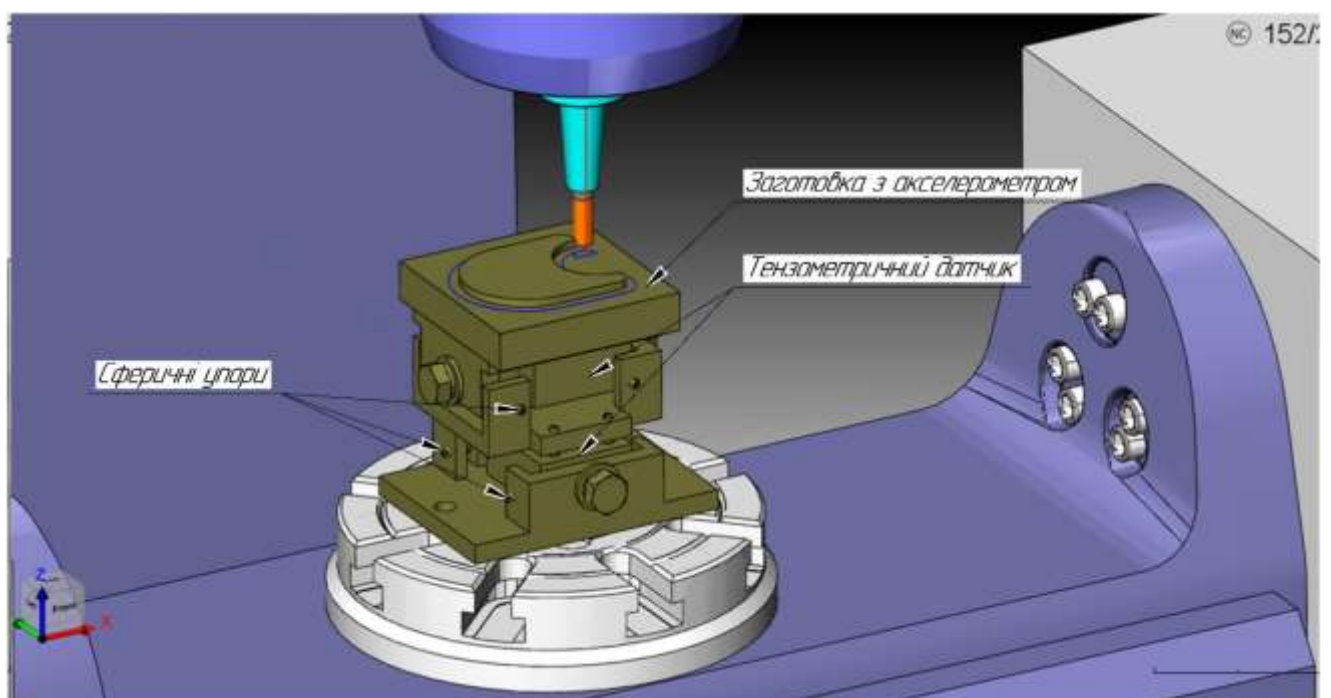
Схема встановлення пристрою на верстаті.
